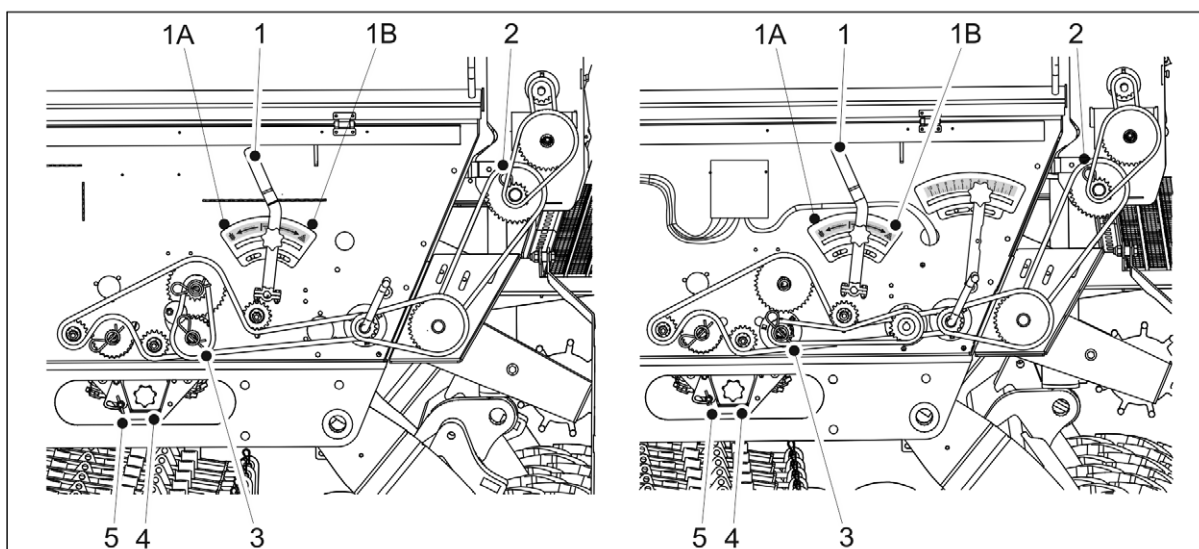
113. Kalibreringsprov med justering av gödselmedlets målshastighet. Till vänster är en maskin utan växellåda och till höger en maskin med en växellåda.
